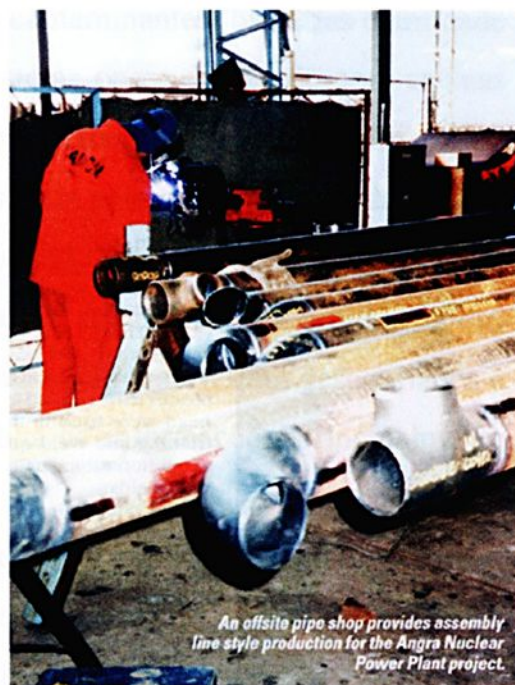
Soldagem orbital em tubos espessos (com adição de arame)
